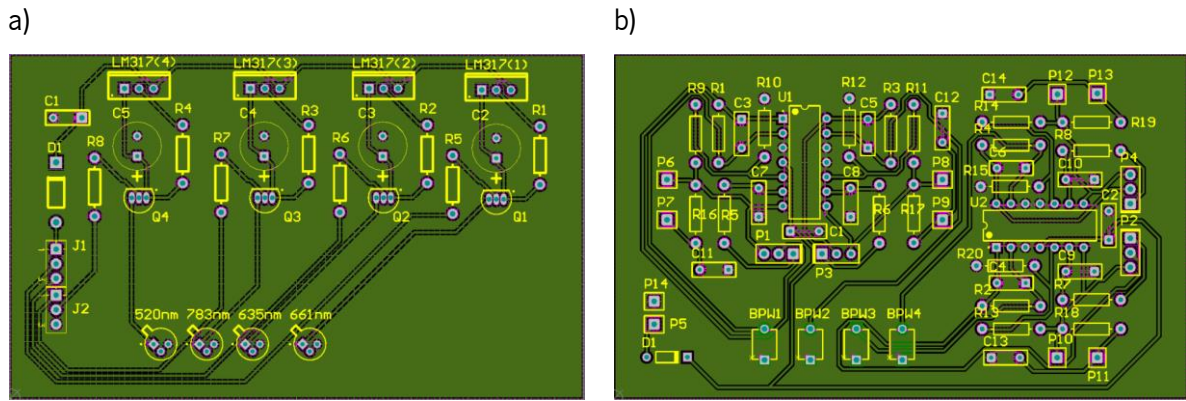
PCBs desenhadas para a primeira configuração do sistema: a) PCB de emissão; b) PCB de recepção. Cada placa tem uma dimensão de 6 cm × 23 cm.
